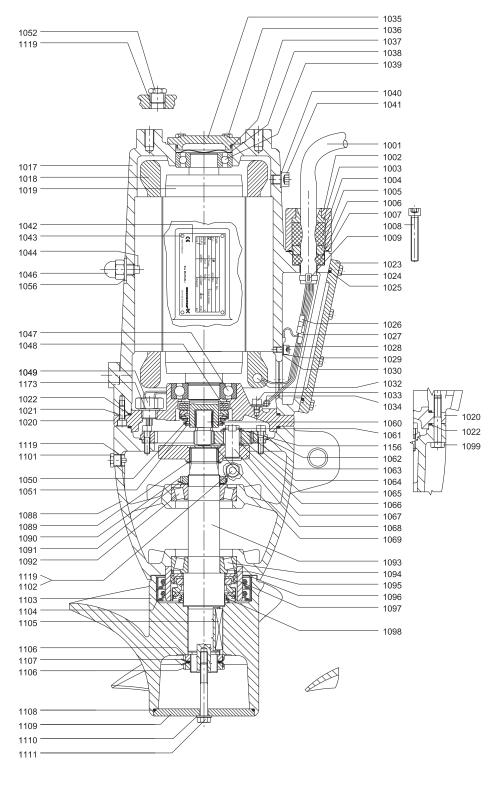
Чертёж в разрезе, SRP.xx.30.xxx
